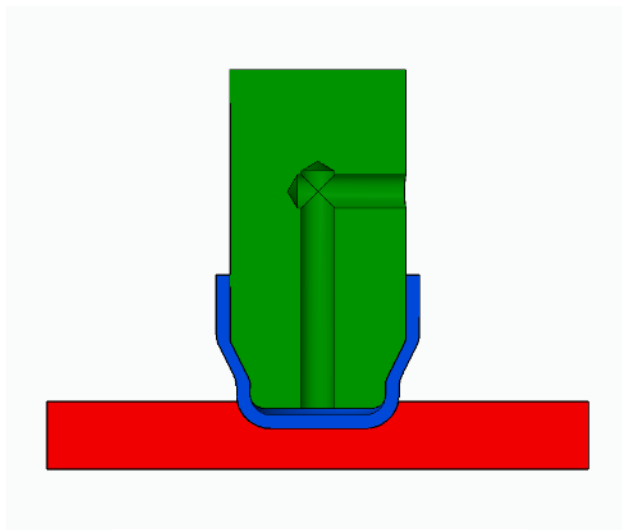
Nástroj pre zlúčené ťahanie výtlačku s prírubou
